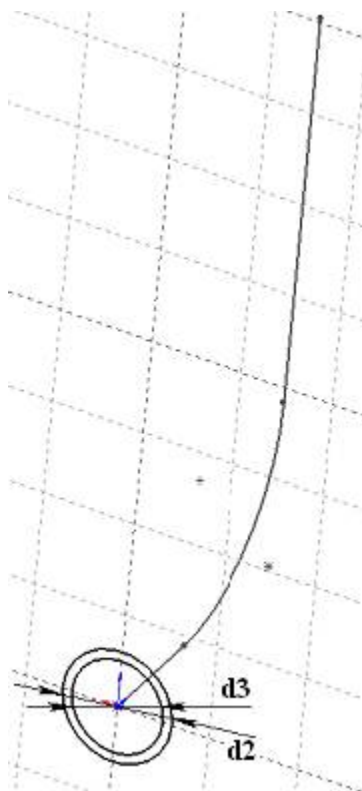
Завдання порожнини в трубі витяжки
